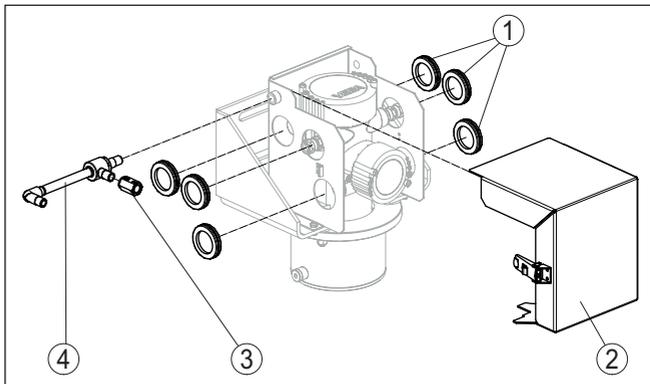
Pezzi di ricambio - raffreddamento ad aria POINTRAC - esecuzione corta (46 mm)
